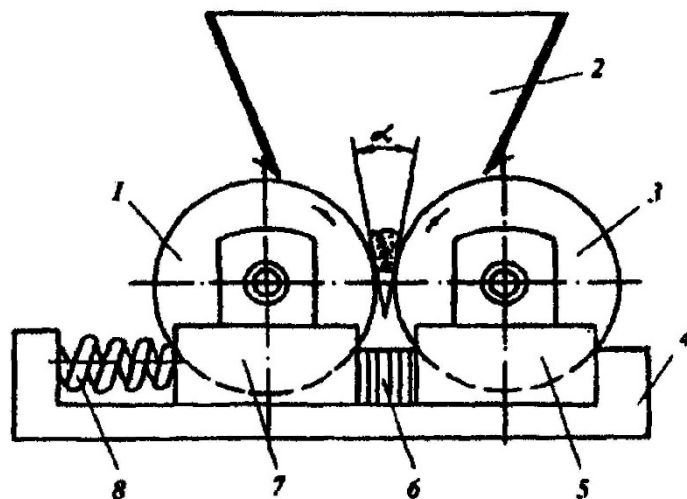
Схема валкової дробарки: 1, 3 – валки; 2 – завантажувальний бункер; 4 – станина; 5, 7 – підшипникові вузли; 6 – прокладки; 8 – пружина
